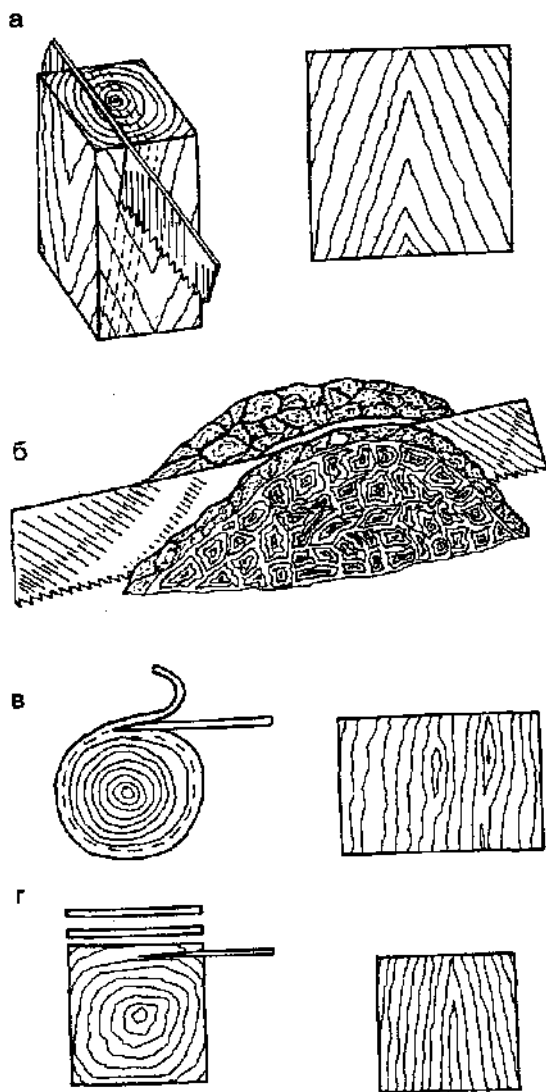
Шпон (схема изготовления и внешний вид): а — пиленный полуторец, б — пиленный каповый; в — лущеный; г — строганный
